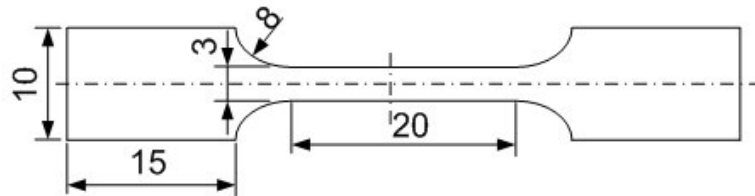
Geometrie der Zugproben. Die Dicke der Zugproben entspricht der Dicke der Bleche
